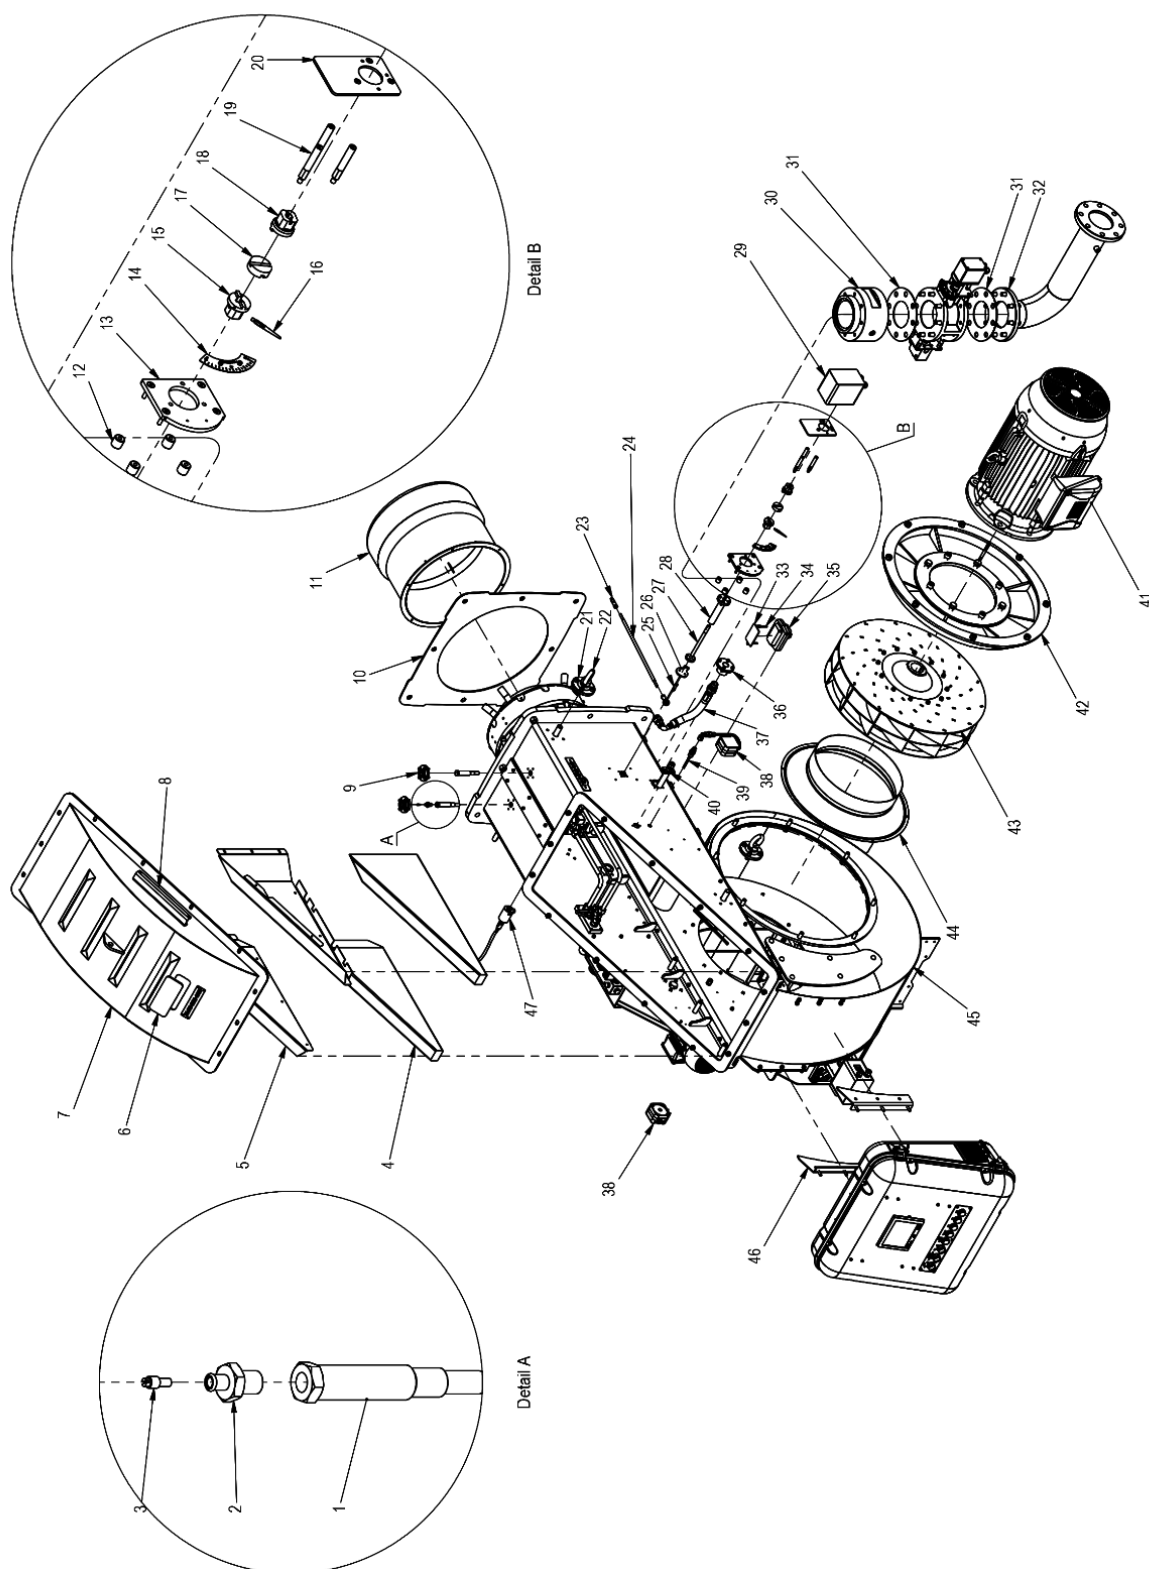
Вид элементов корпуса и вентилятора горелки RGB-M-1350
